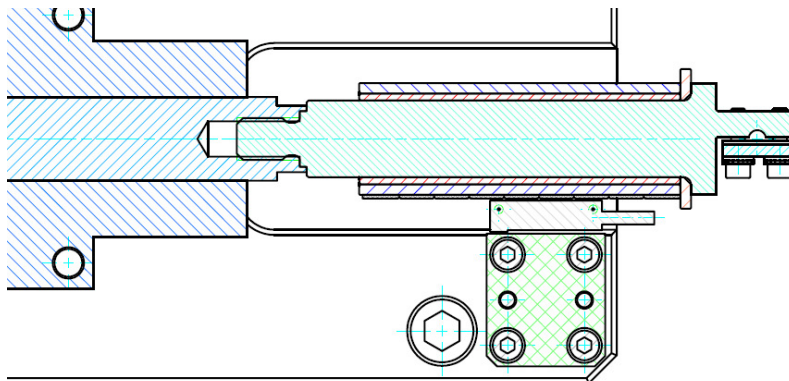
Schnittzeichnung Temperaturkompensation Glasmessstab
